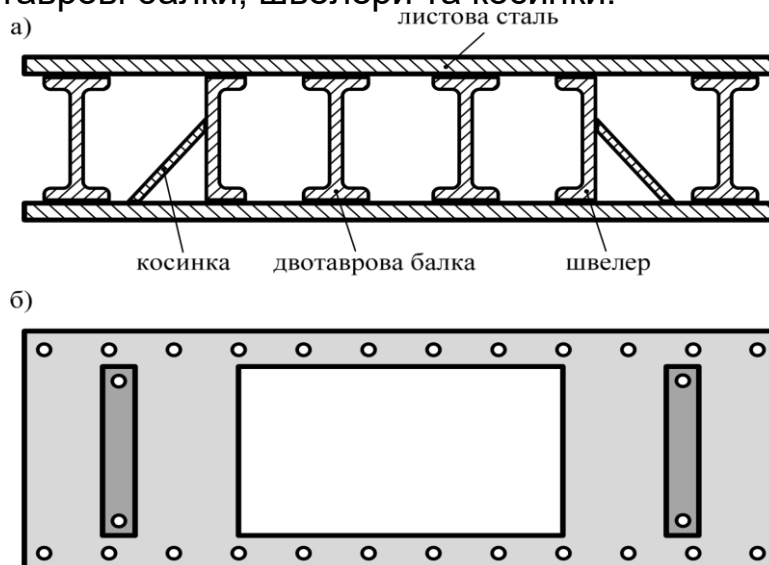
Фундаментна плита: розріз (а); вигляд зверху (б)
